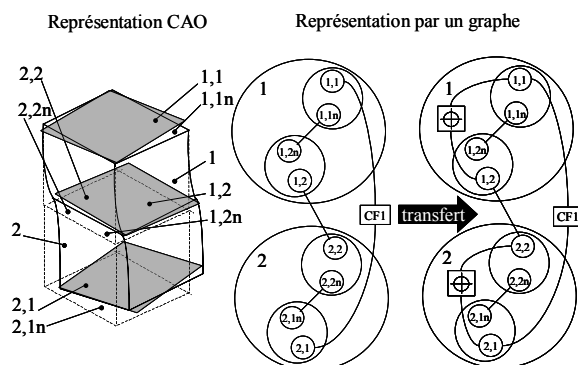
Position relative entre deux surfaces de substitution d'un assemblage de pièces chaudes.
